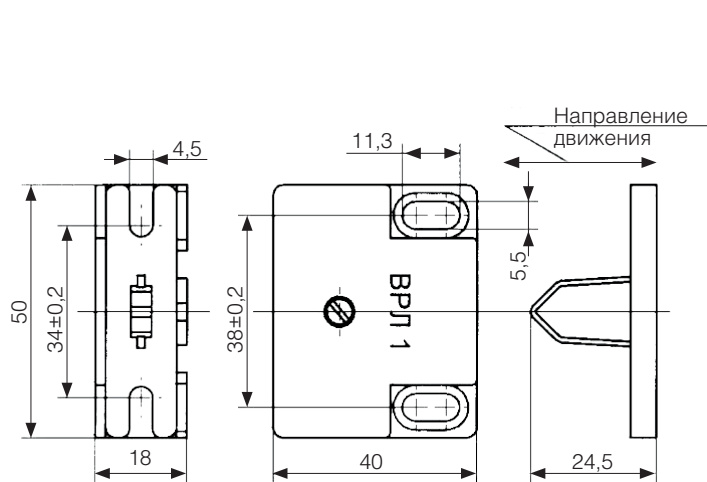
Габаритные, установочные и присоединительные размеры ВРЛ 1
